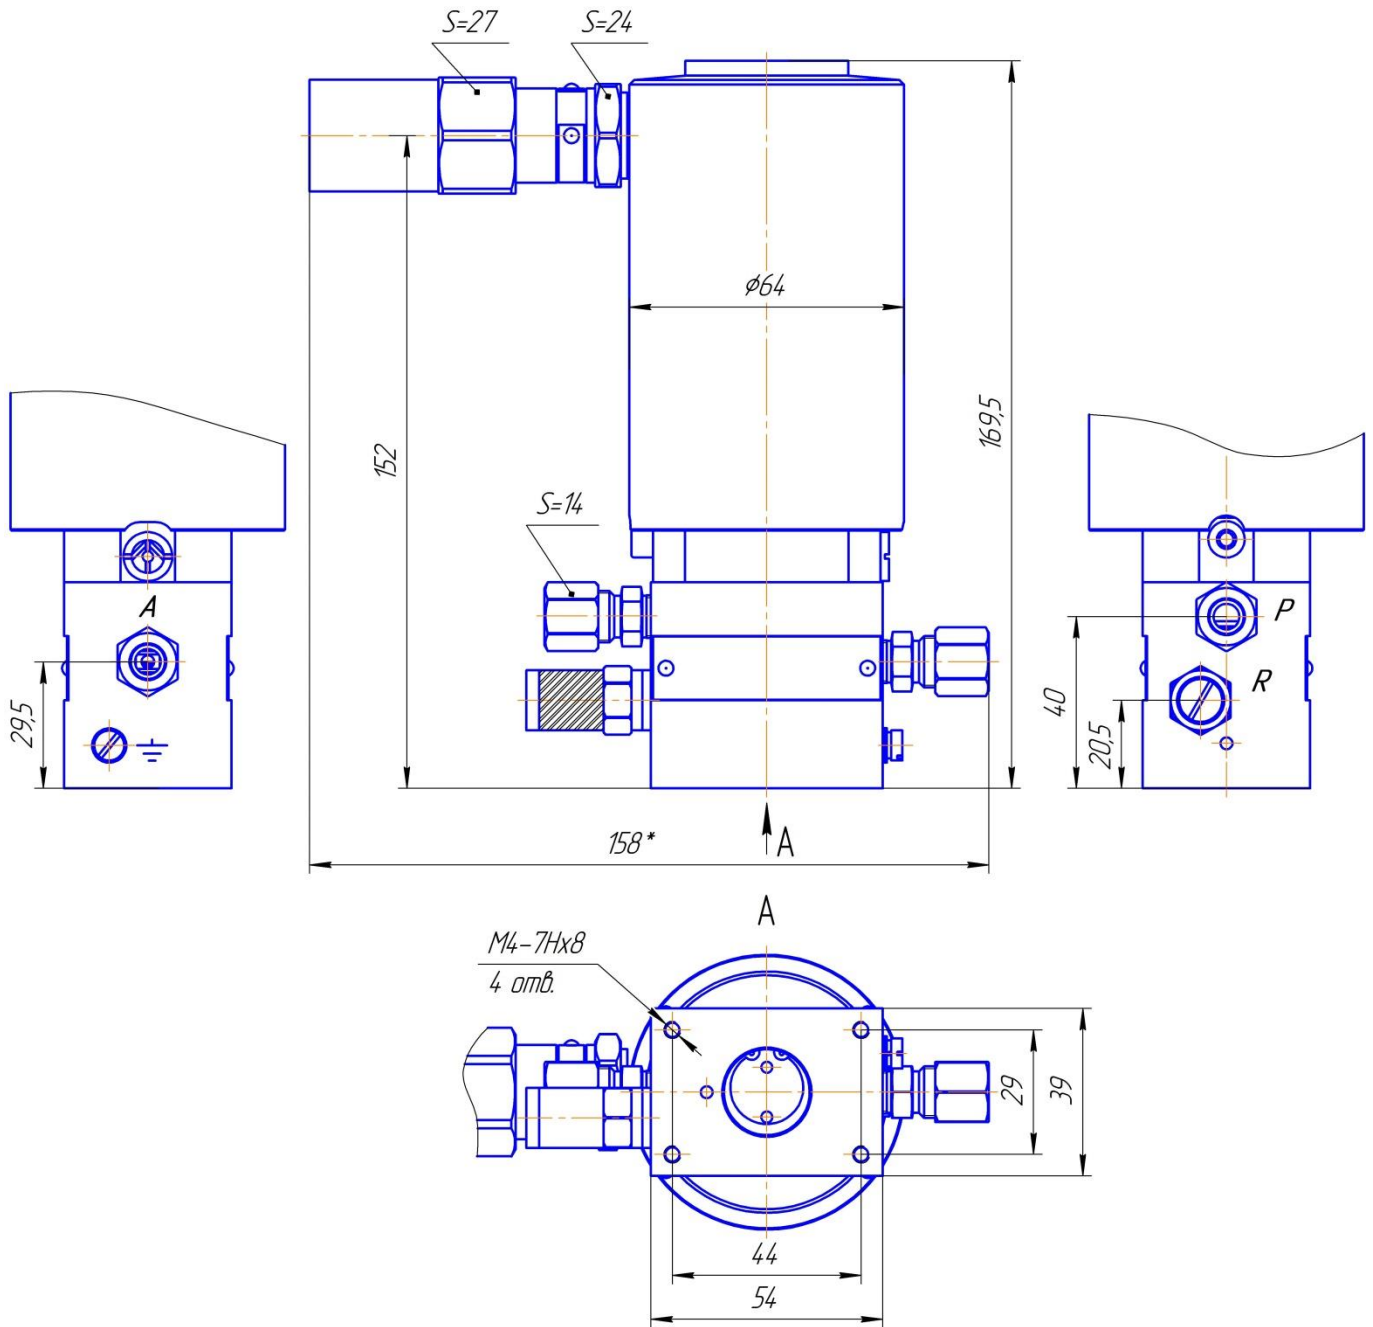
Габаритные и установочные размеры исполнений клапана КРВ-М-3/2-Т-ПД с кабельным вводом для монтажа кабеля в металлорукаве РЗ-ЦХ-15
